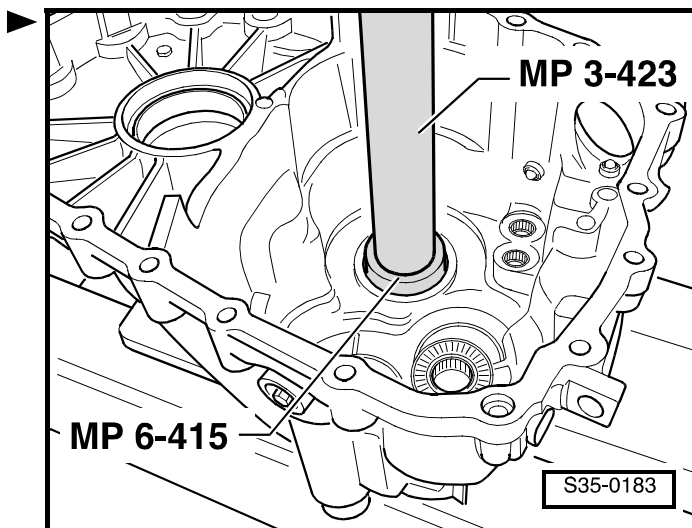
Запрессовывание наружной обоймы конического роликоподшипника в картер коробки передач
